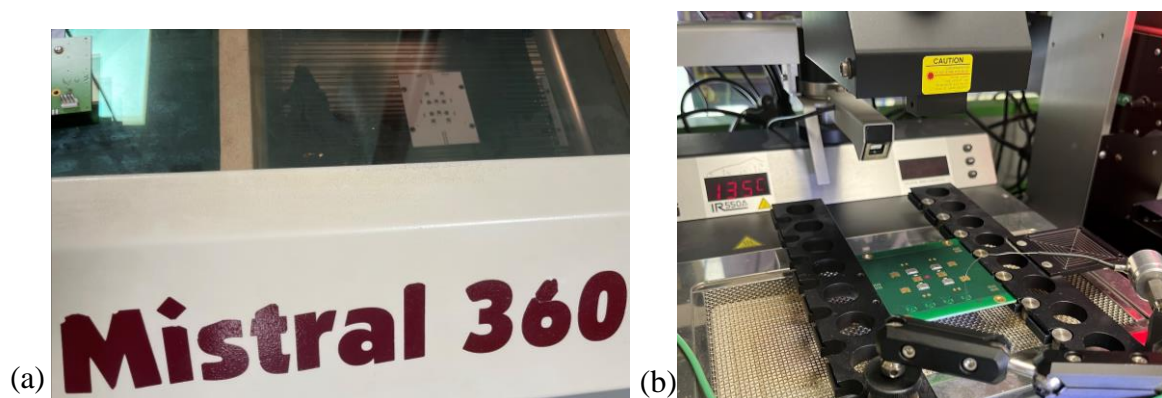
Brasage des MOSFETs (a) par le four sur le SMI (b) par la machine BGA sur le PCB
